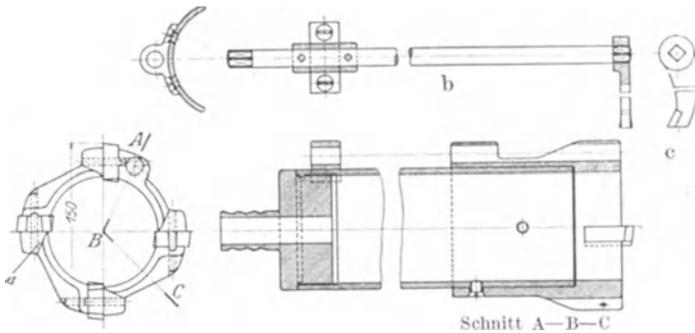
Hohlbohrer mit Abstechvorrichtung.
